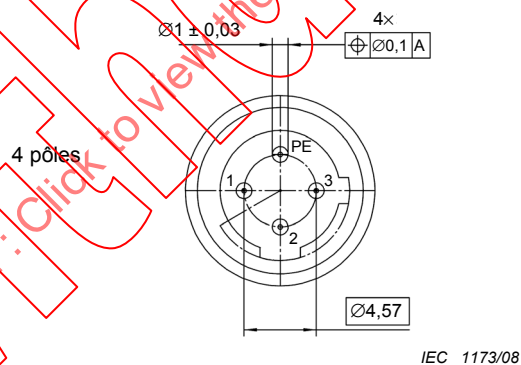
Vue de face du contact mâle, 4 pôles, codage C
